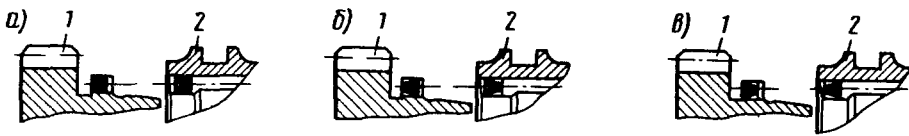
Контакт венца синхронизатора шестерни и муфты:
